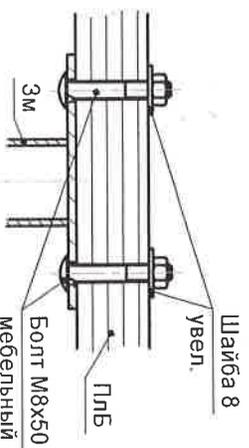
Крепление змейки (Зм) к площадкам башен (ПлБ)
